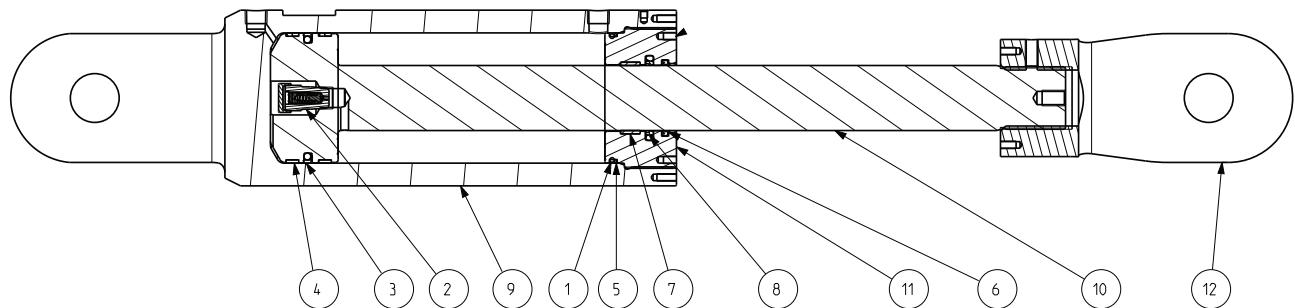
Hauptkomponenten Zugzylinder (erste Ansicht)
